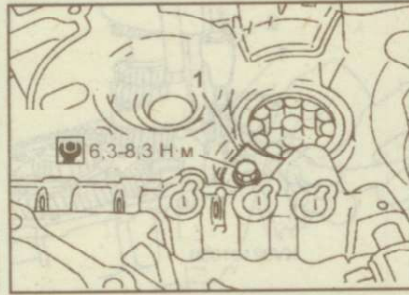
Установка держателя (1) переднего подшипника вторичного вала
